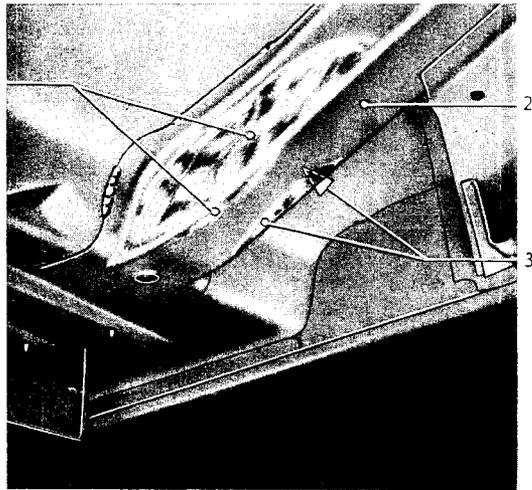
Anlageflächen am rechten Hinterlängsträger für beide Hinterfederstützen blankgeschliffen
